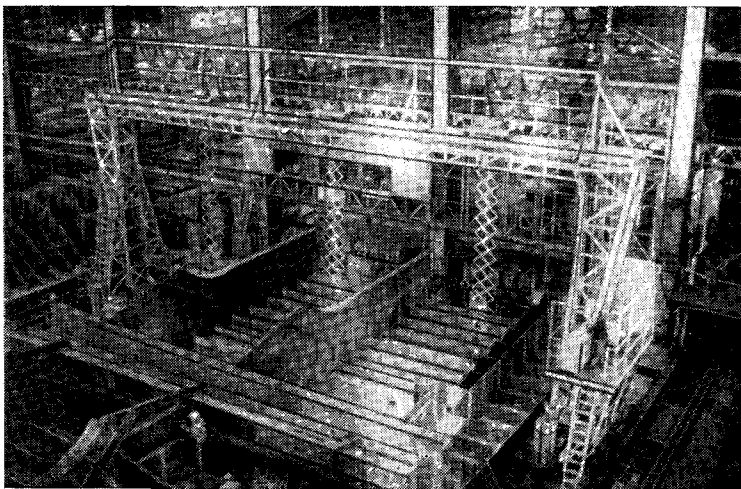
Агрегат автоматической сварки решеток набора и полотнищ листов, применяемый компанией «Мицубиси хэви индастриз».
